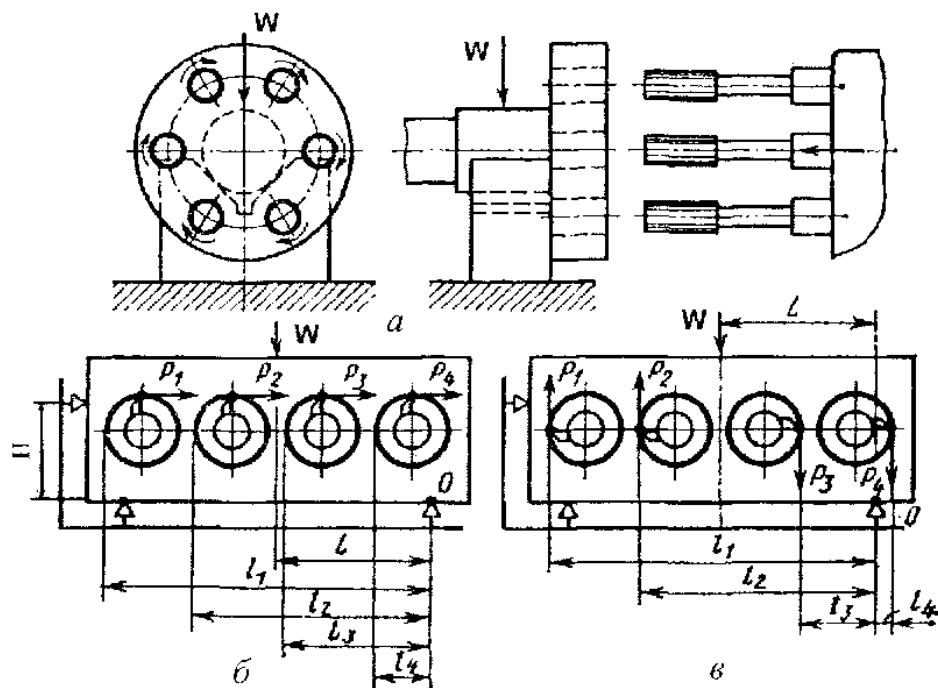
Схеми для визначення сил закріплення заготовок при багатоінструментальній обробці
